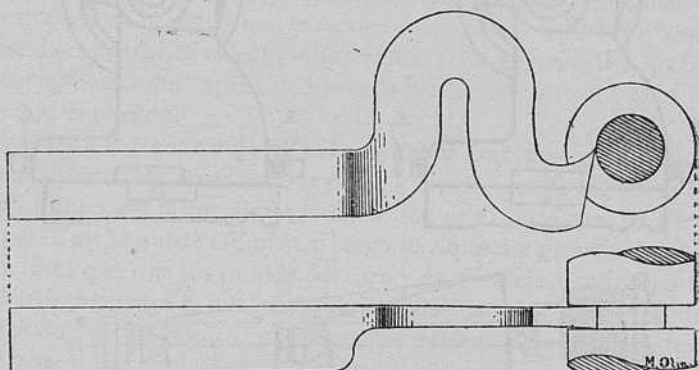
Herramienta para trocear cortando por la parte superior.
